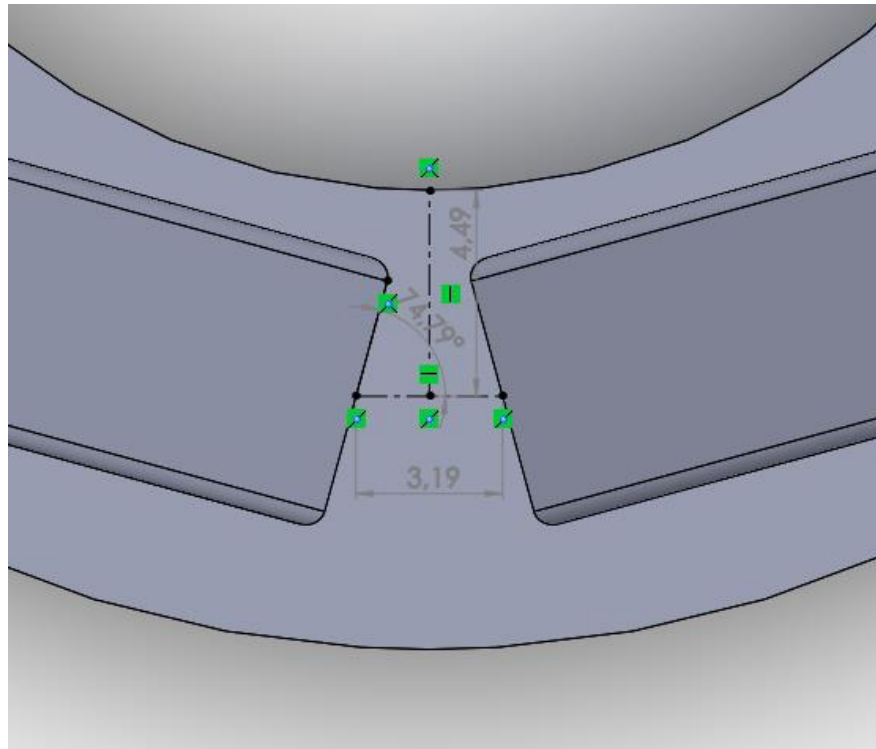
Parámetros de ubicación de los perfiles en el anillo metálico
